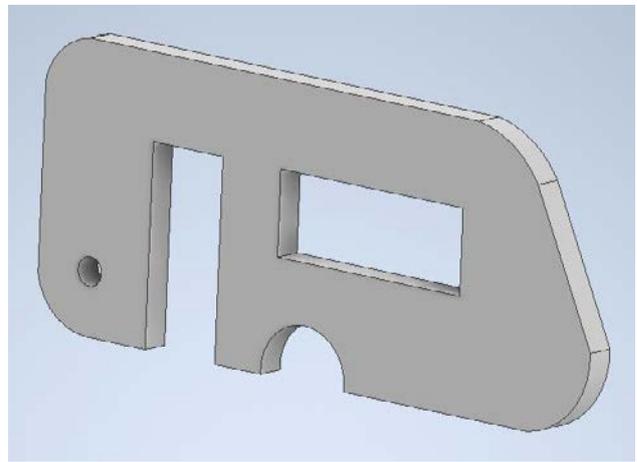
CAD-Zeichnung einer Caravan-Seitenwand
